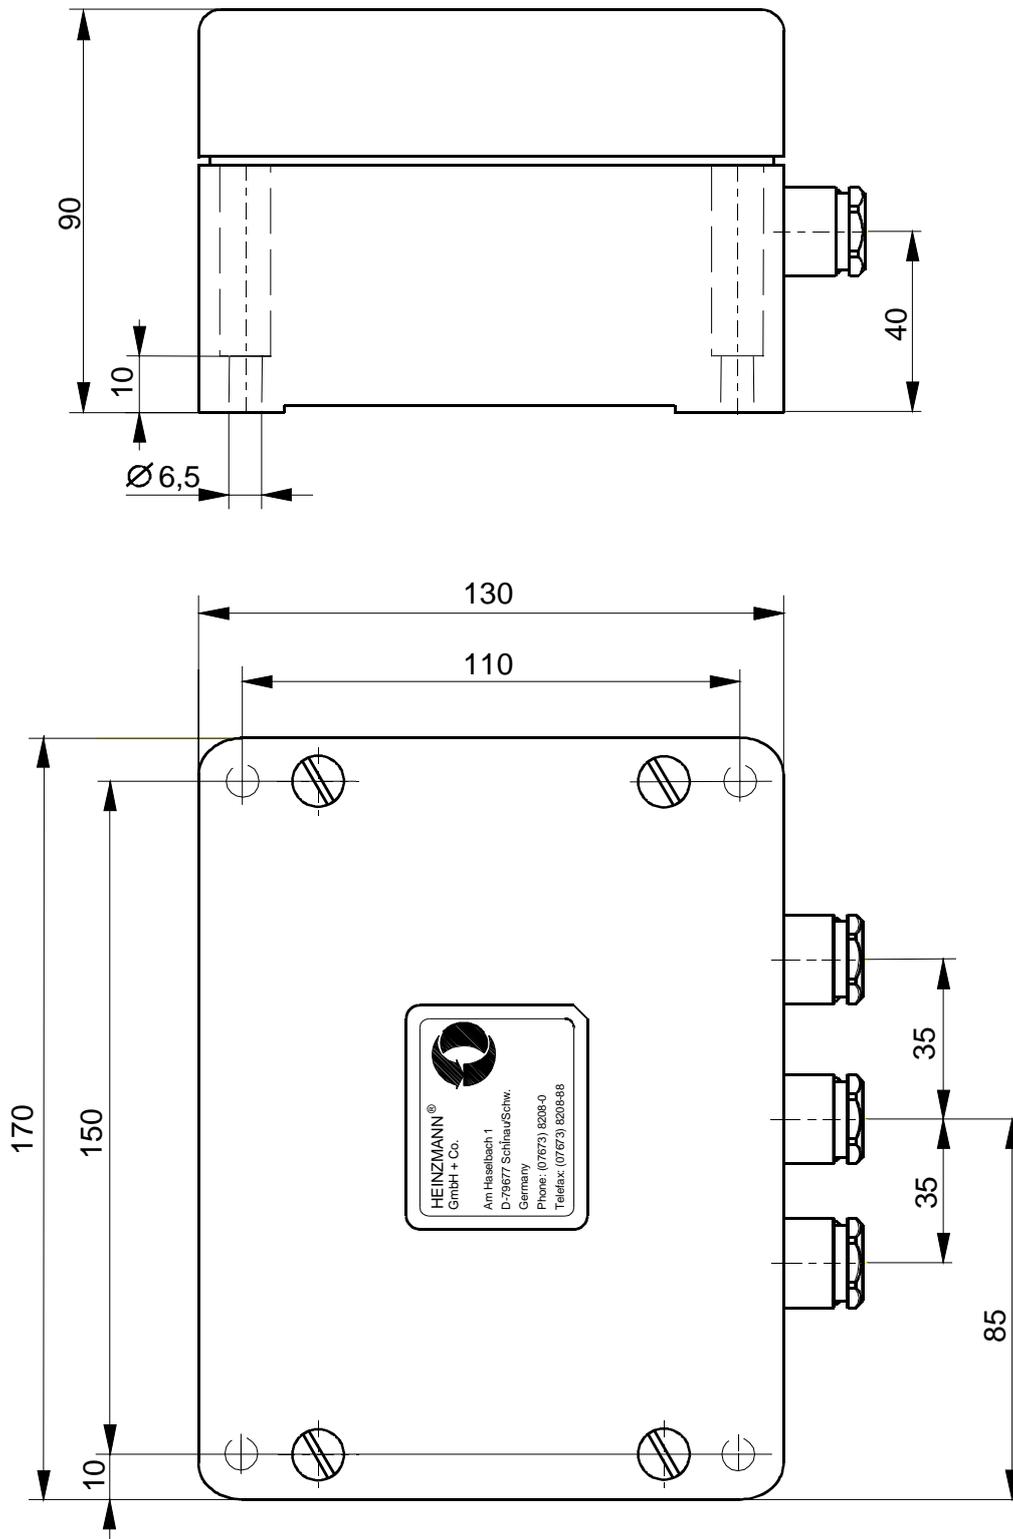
Maßzeichnung ESW 01 mit Metallgehäuse IP 55
